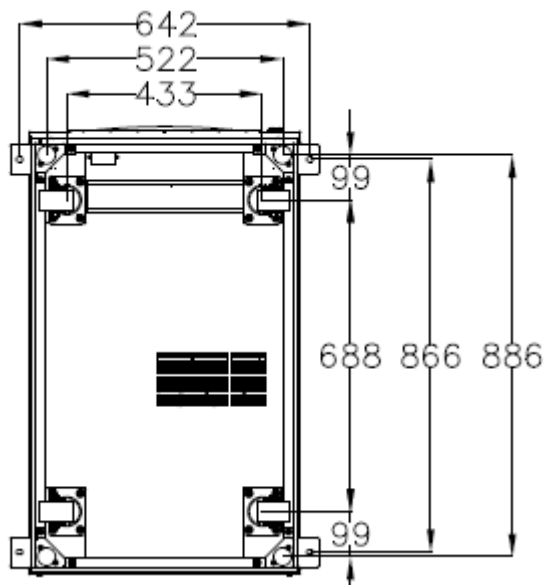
Опорная конструкция 60кВА, 90кВА и 120кВА (вид снизу, единицы: мм)
